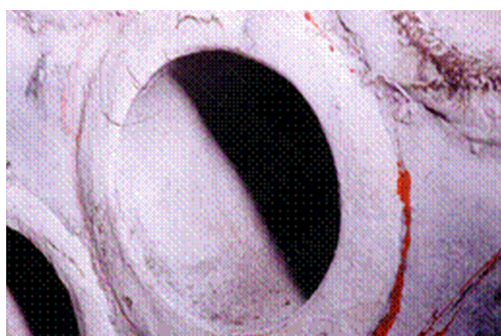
Ensayo no destructivo demuestra fisuras
